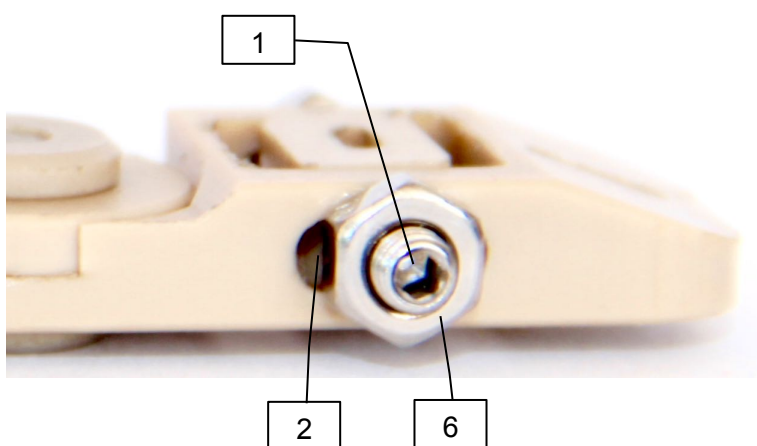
modifizierter proximaler Schenkel Ligtrac Version 2 mit Bezeichnung der technischen Teile, Aufsicht. Bezeichnungen vgl. Tab 17.
